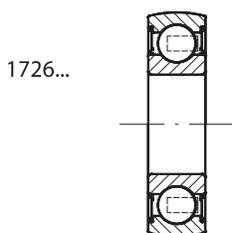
Регулируемые шариковые подшипники – тип 1726...
